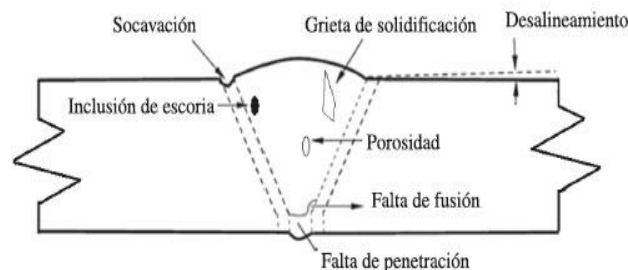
Imperfecciones de soldadura en juntas a tope. Fuente: Maddox (1994).
